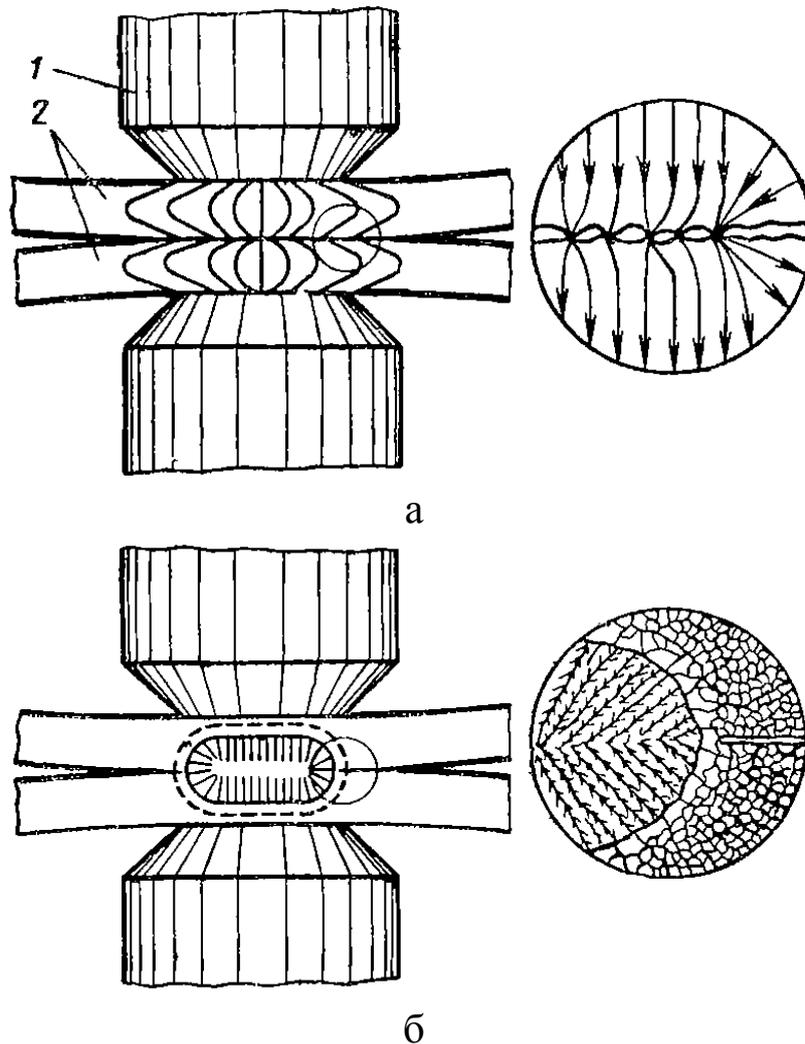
Формирование сварного соединения при точечной сварке (1 – электрод, 2 – детали)
